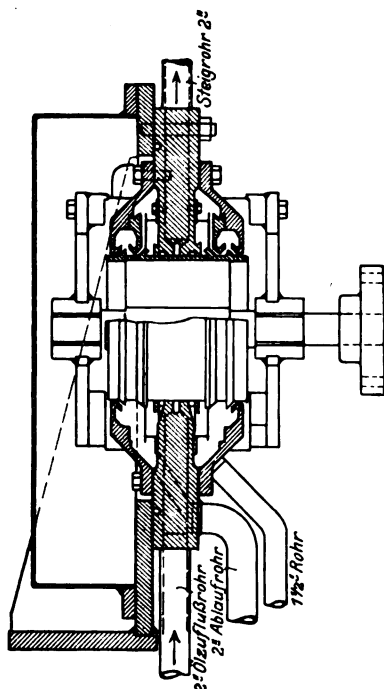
Schnitt durch die Öldichtung. Ausführung 1.
